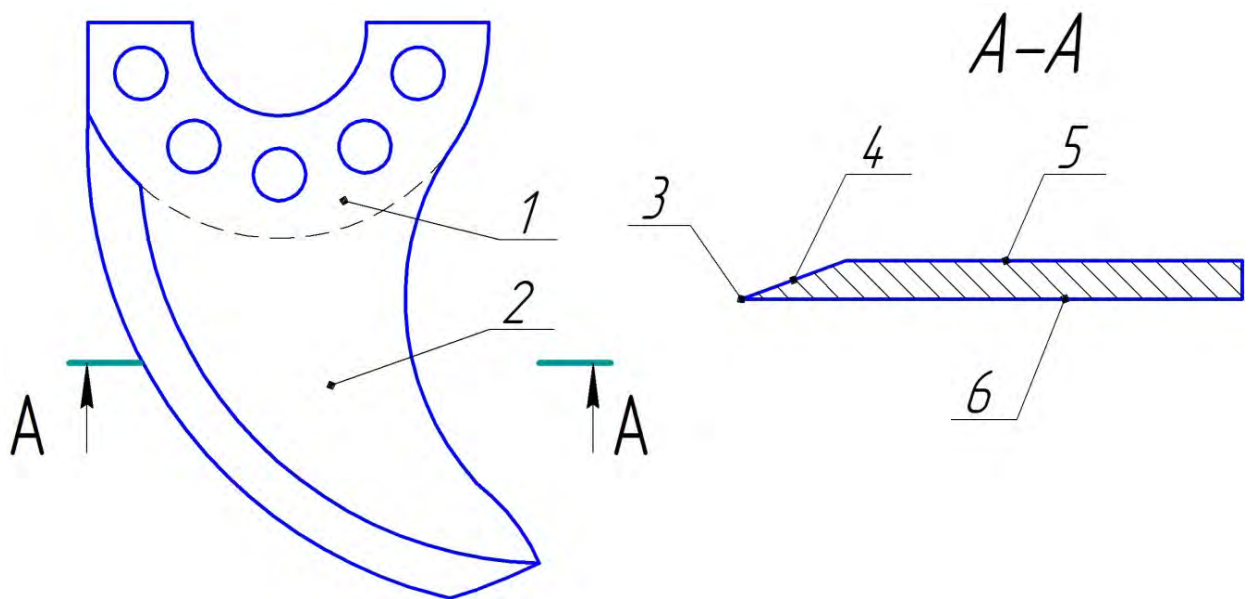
Будова ножа кутера: 1 - посадочна частина корпусу; 2 - робоча частина корпусу; 3 - різальний крайок; 4 - передня поверхня леза; 5 - верхня поверхня корпусу; 6 - нижня поверхня корпусу
